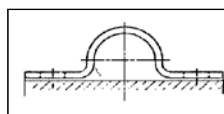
Příklad prvku rozvodných potrubí (spojka přímá, hydraulická hadice)
